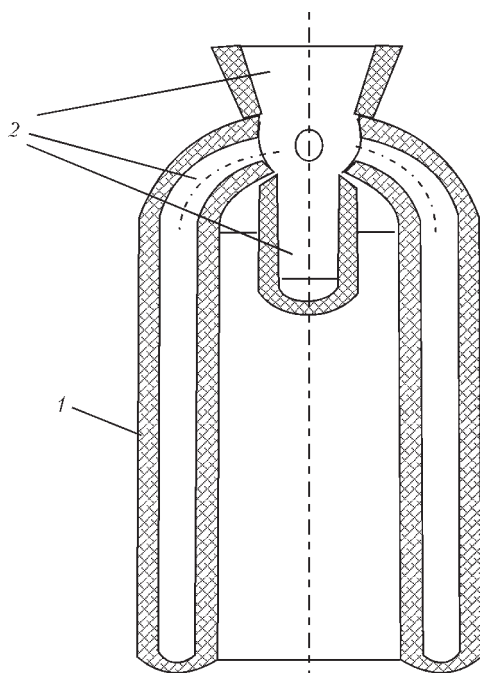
Схема керамической оболочковой формы для отливки трубных заготовок: 1 — цилиндрическая оболочковая часть; 2 — литниково-питающая система с заливочной чашей
